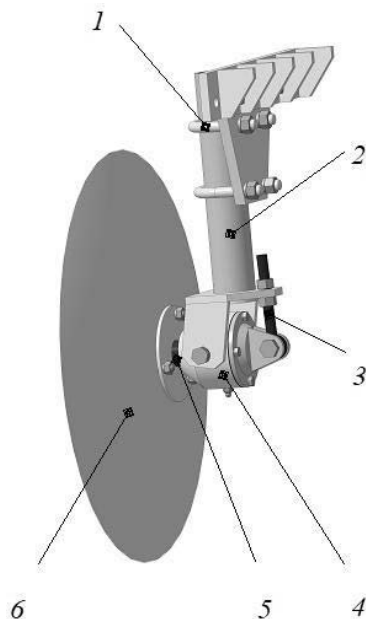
Общий вид экспериментального образца дискового предплужника: 1 – скоба; 2 – стойка; 3 – натяжник; 4 – подшипниковый узел; 5 – ось; 6 – сферический диск
